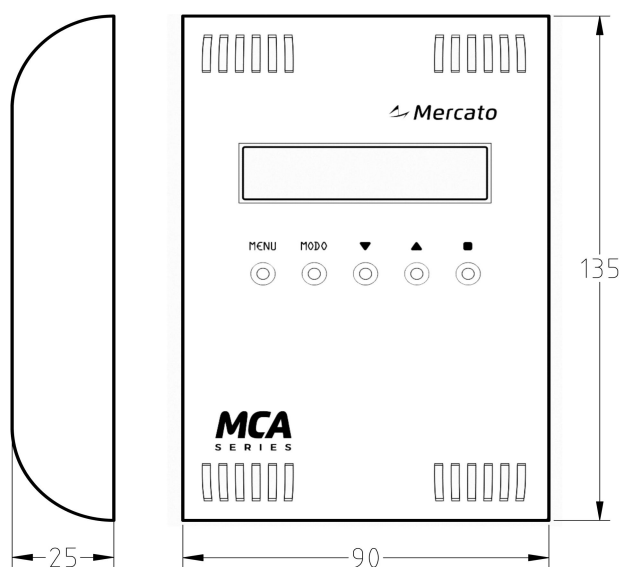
Dimensões da face do produto, em milímetros (mm).
